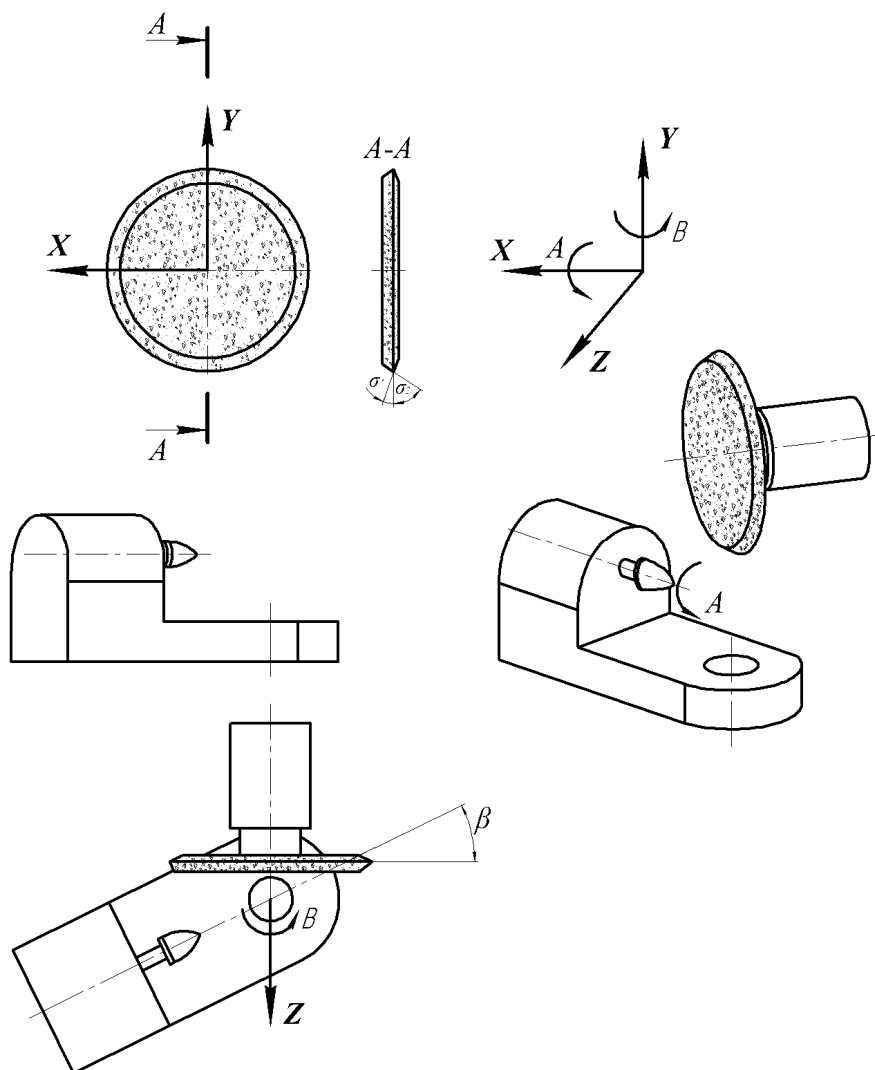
Схема обработки на шлифовально-заточных станках с ЧПУ
